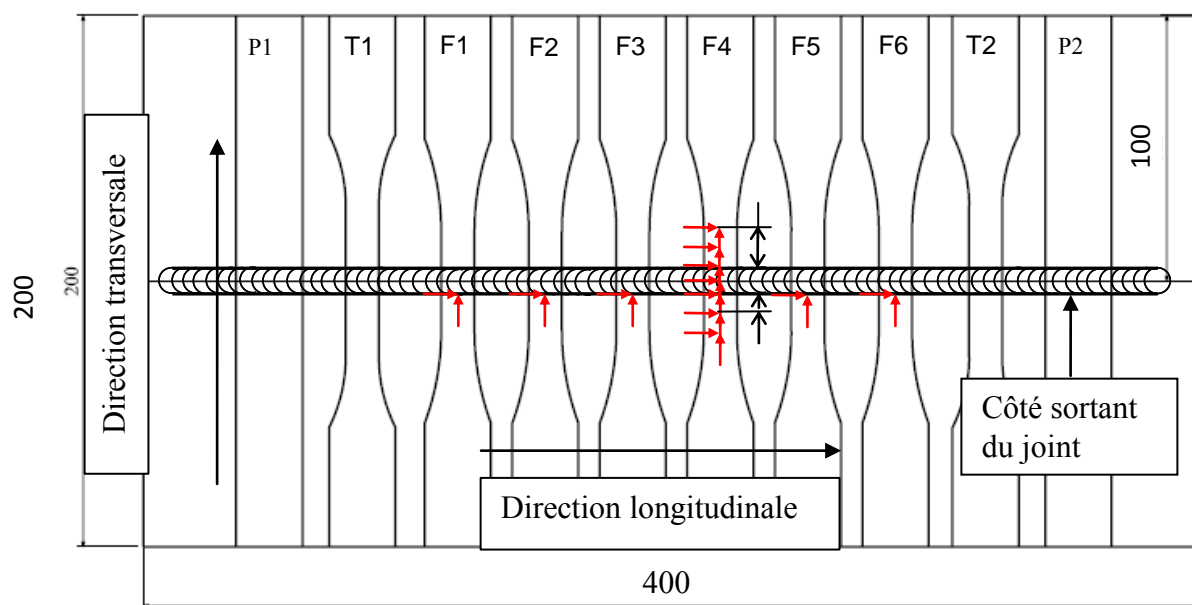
Emplacement et directions des mesures des contraintes résiduelles sur une plaque brute de soudage (dimensions en mm).
